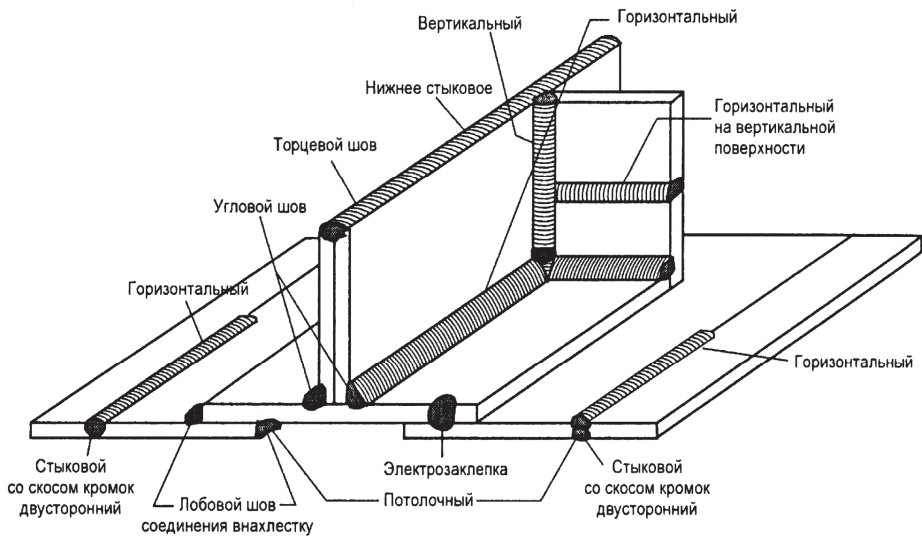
Типы сварных швов и их положение в пространстве
